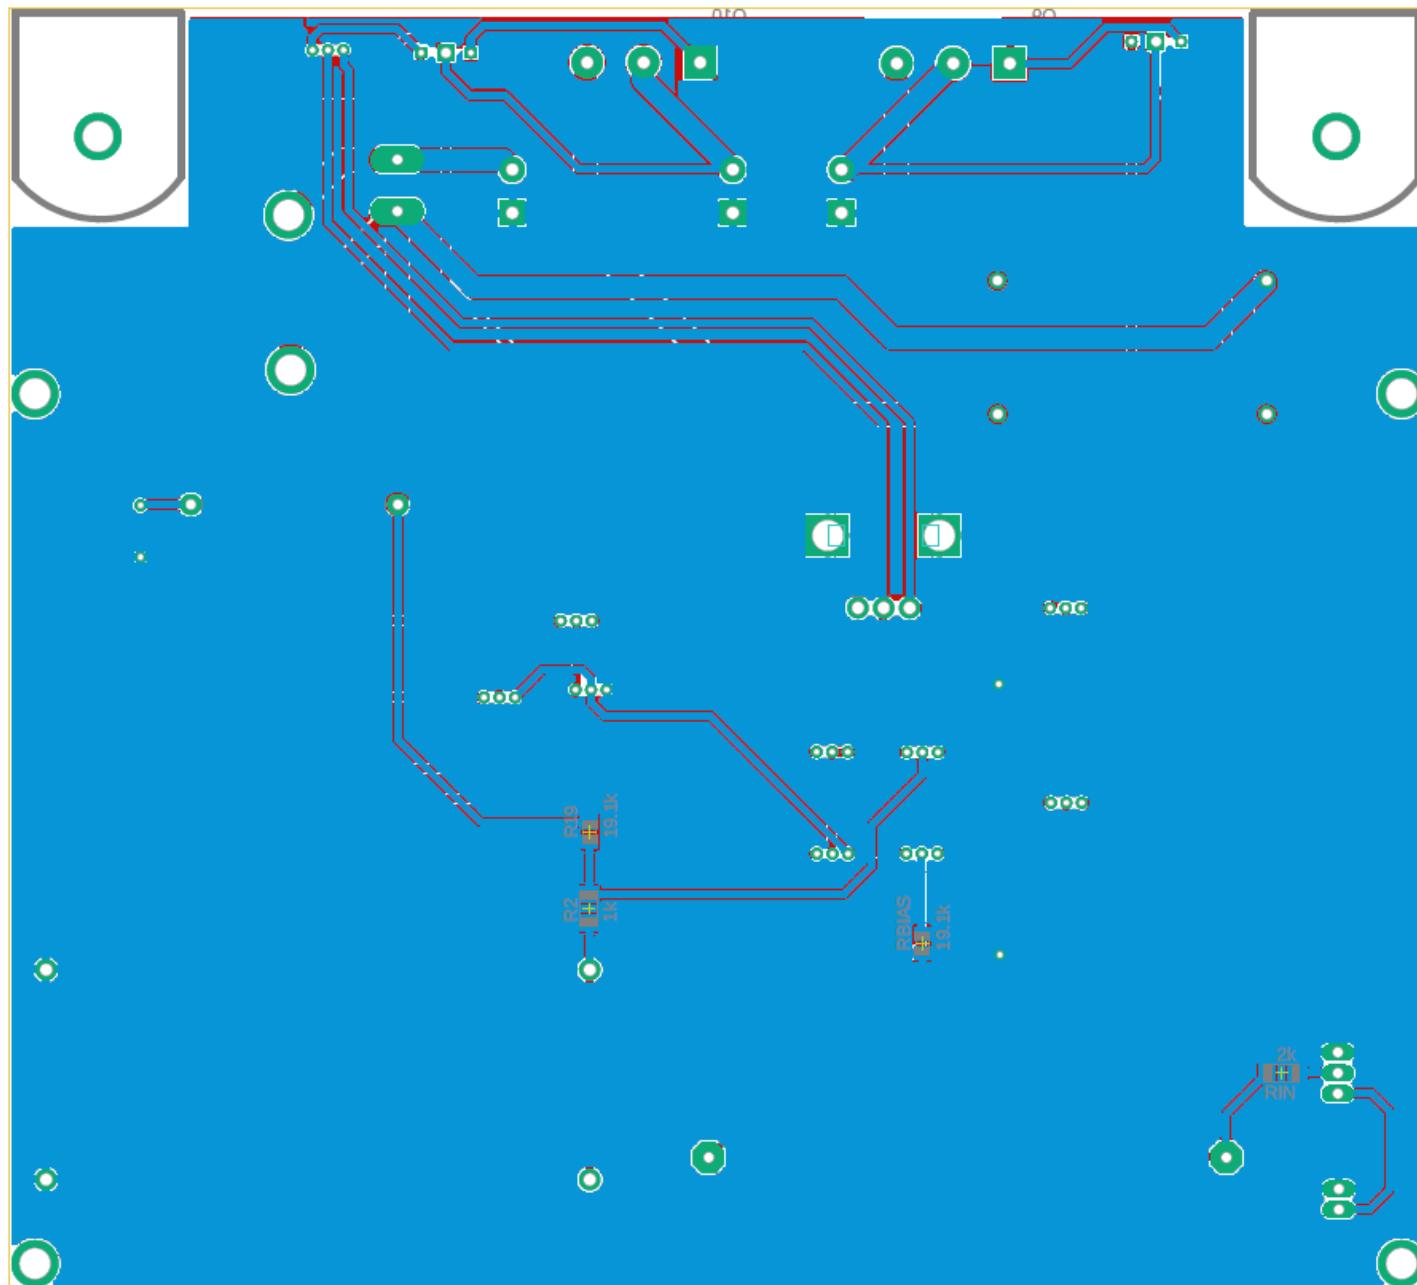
Vista de la cara inferior (“Bottom”) de la PCB.
